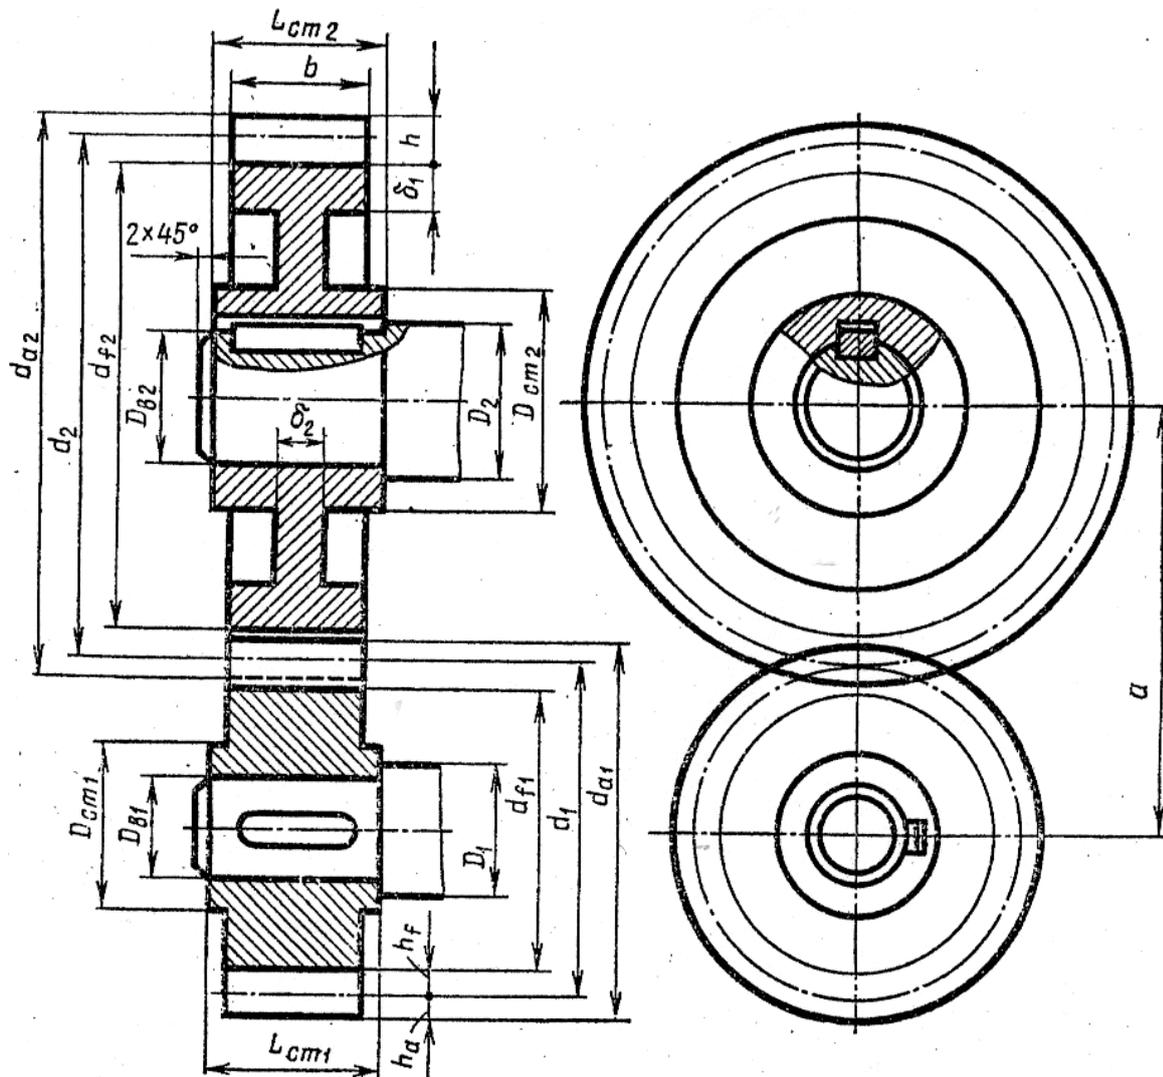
Размеры цилиндрической зубчатой передачи
